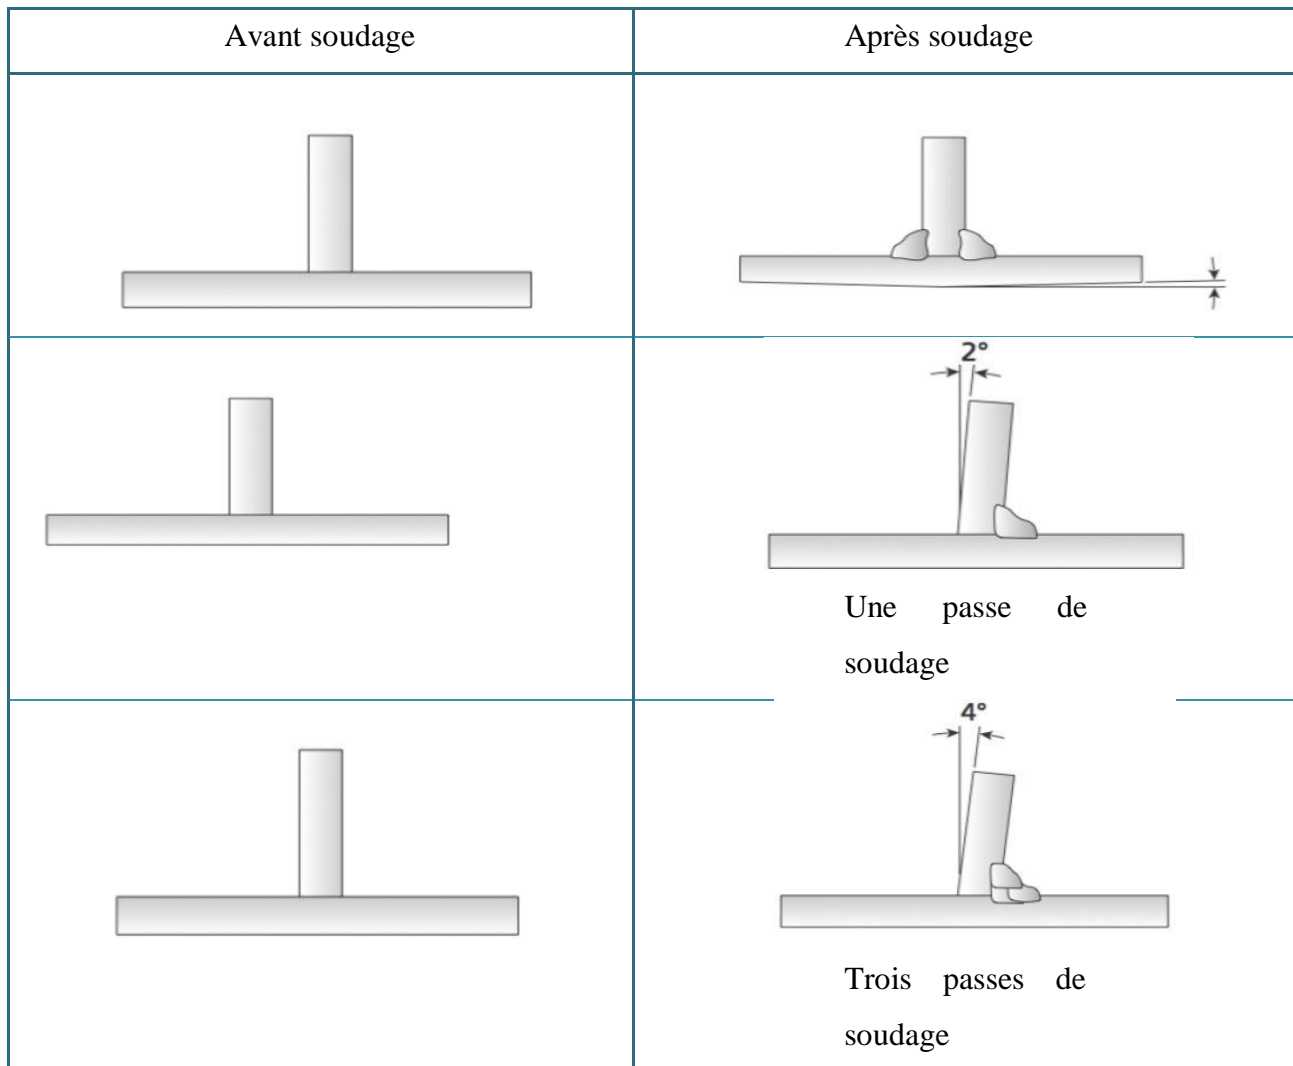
Déformations de soudage d'assemblages en T [48]
